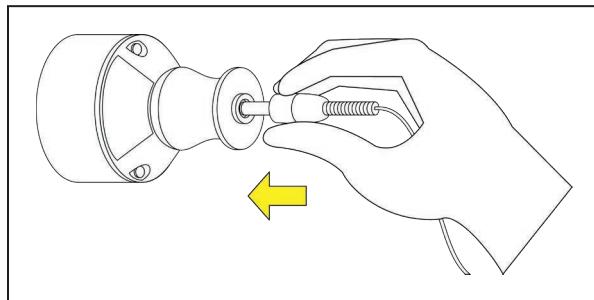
Inserção do conector do adaptador CA no módulo de alimentação.
